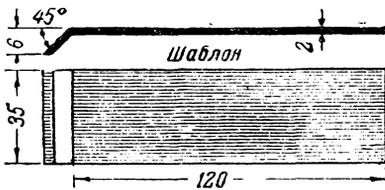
Шаблон для проверки расположения ролика установки кадра
